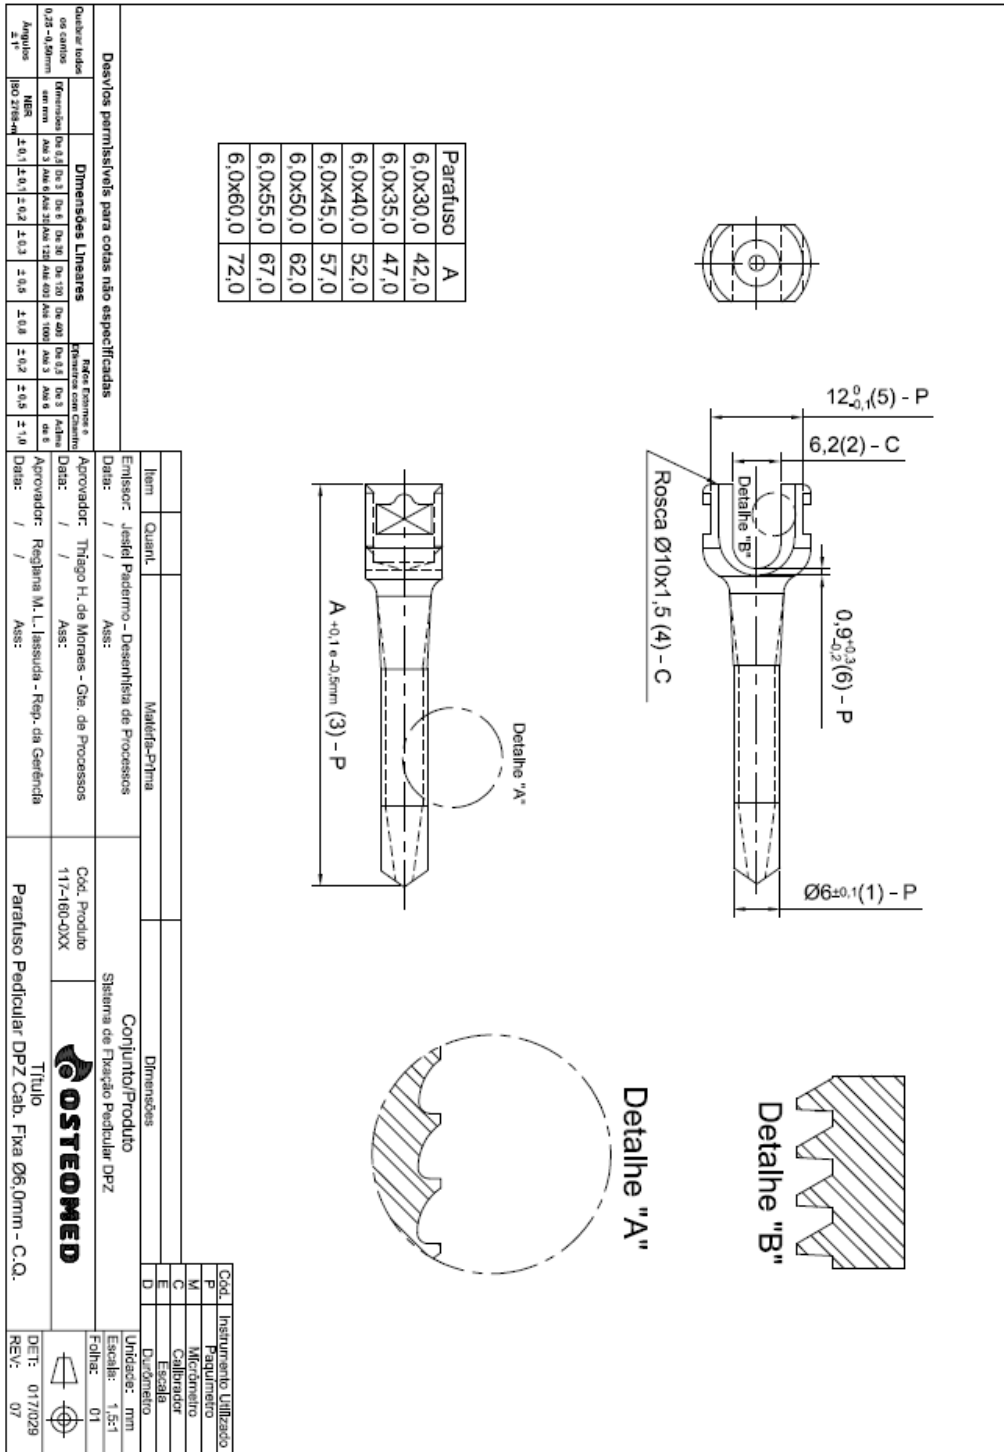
Desenho Técnico do Parafuso Pedicular Cabeça Fixa.
